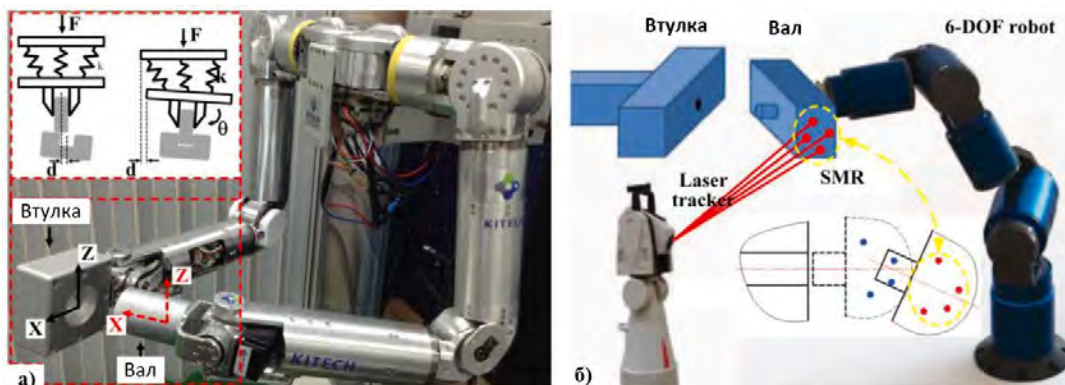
а-робот для поиска сборки с двумя рычагами, пассивной гибкостью, управляемый роботом [6]; б- Система поиска сборки с лазерным наведением на помехи [5].
